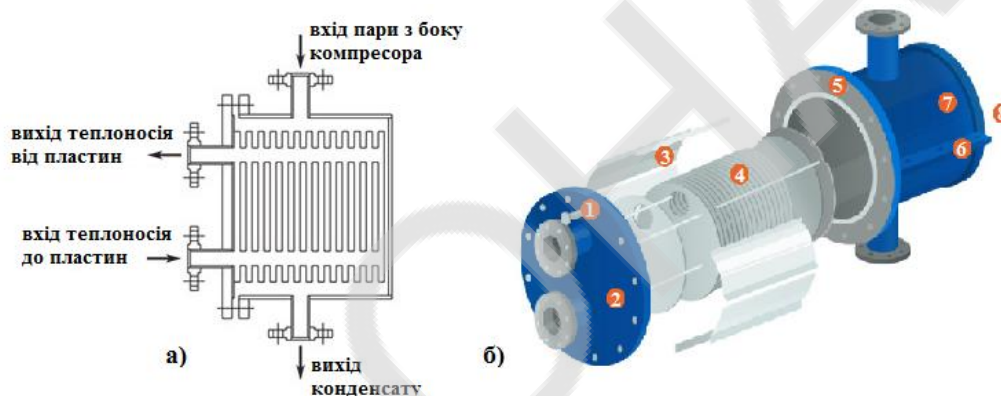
Кожухопластинчастий конденсатор: а) – схема руху потоків; б) – загальний вигляд.
